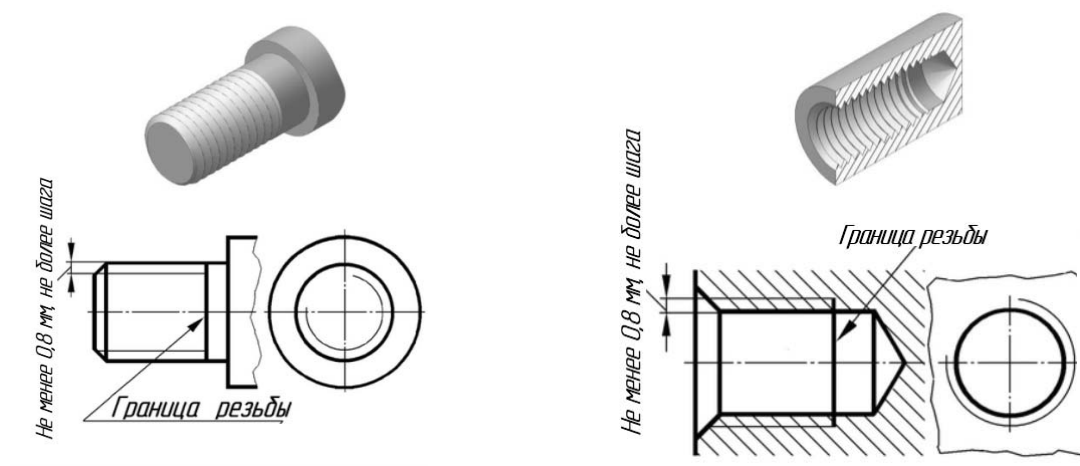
Изображение резьбы на цилиндрических поверхностях
